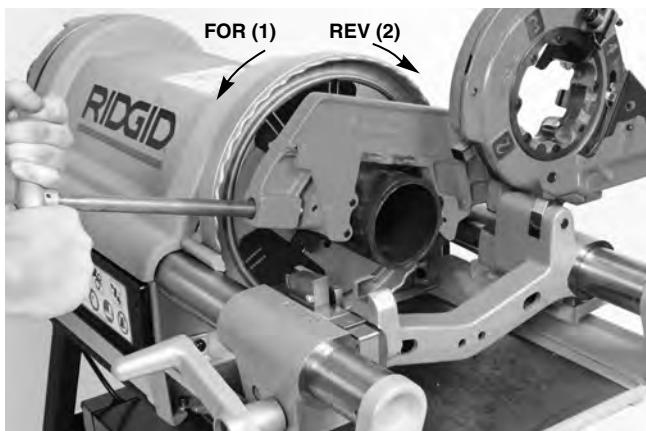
Utilisation du coupe-tubes n° 764 et sens de rotation de la machine
